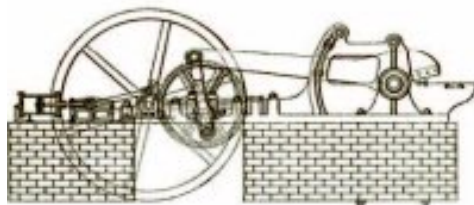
Punzonadora accionada mediante pistón de máquina a vapor.¹⁴
